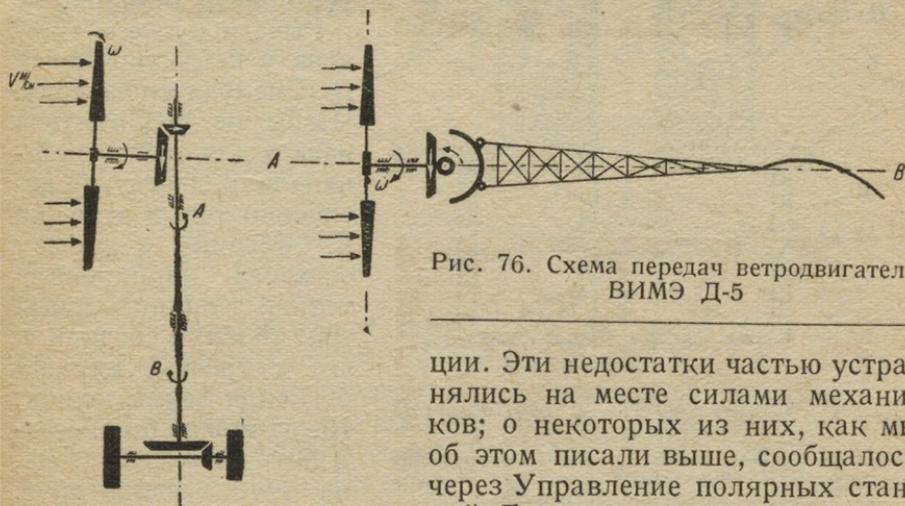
Схема передач ветродвигателя ВМЭ Д-5
